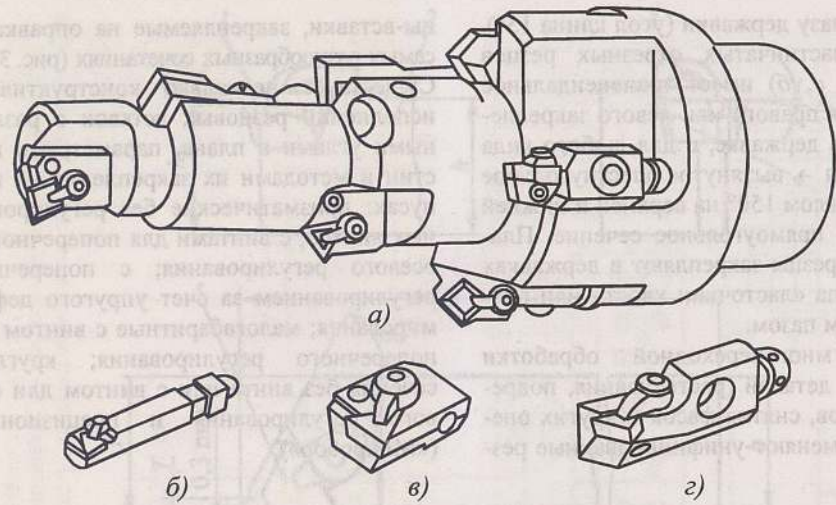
Комбинированный расточной инструмент: а – оправка; б – удлиненный регулируемый резец-вставка; в – нерегулируемый резец-вставка; г – короткий регулируемый резец-вставка
